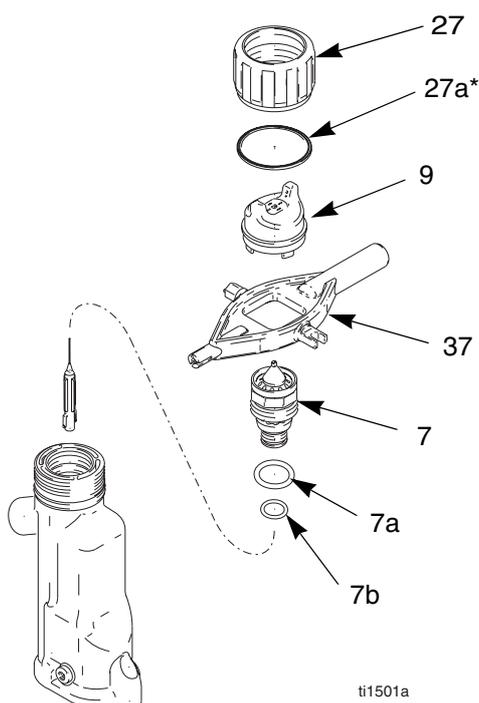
Remplacement de l'ensemble chapeau d'air/buse
